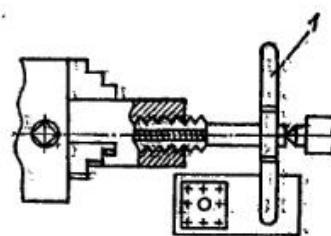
Нарезание резьбы с креплением метчика в слесарном воротке
